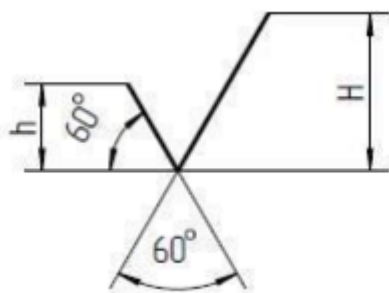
Знак шероховатости, когда метод образования поверхности чертежом не регламентируется
